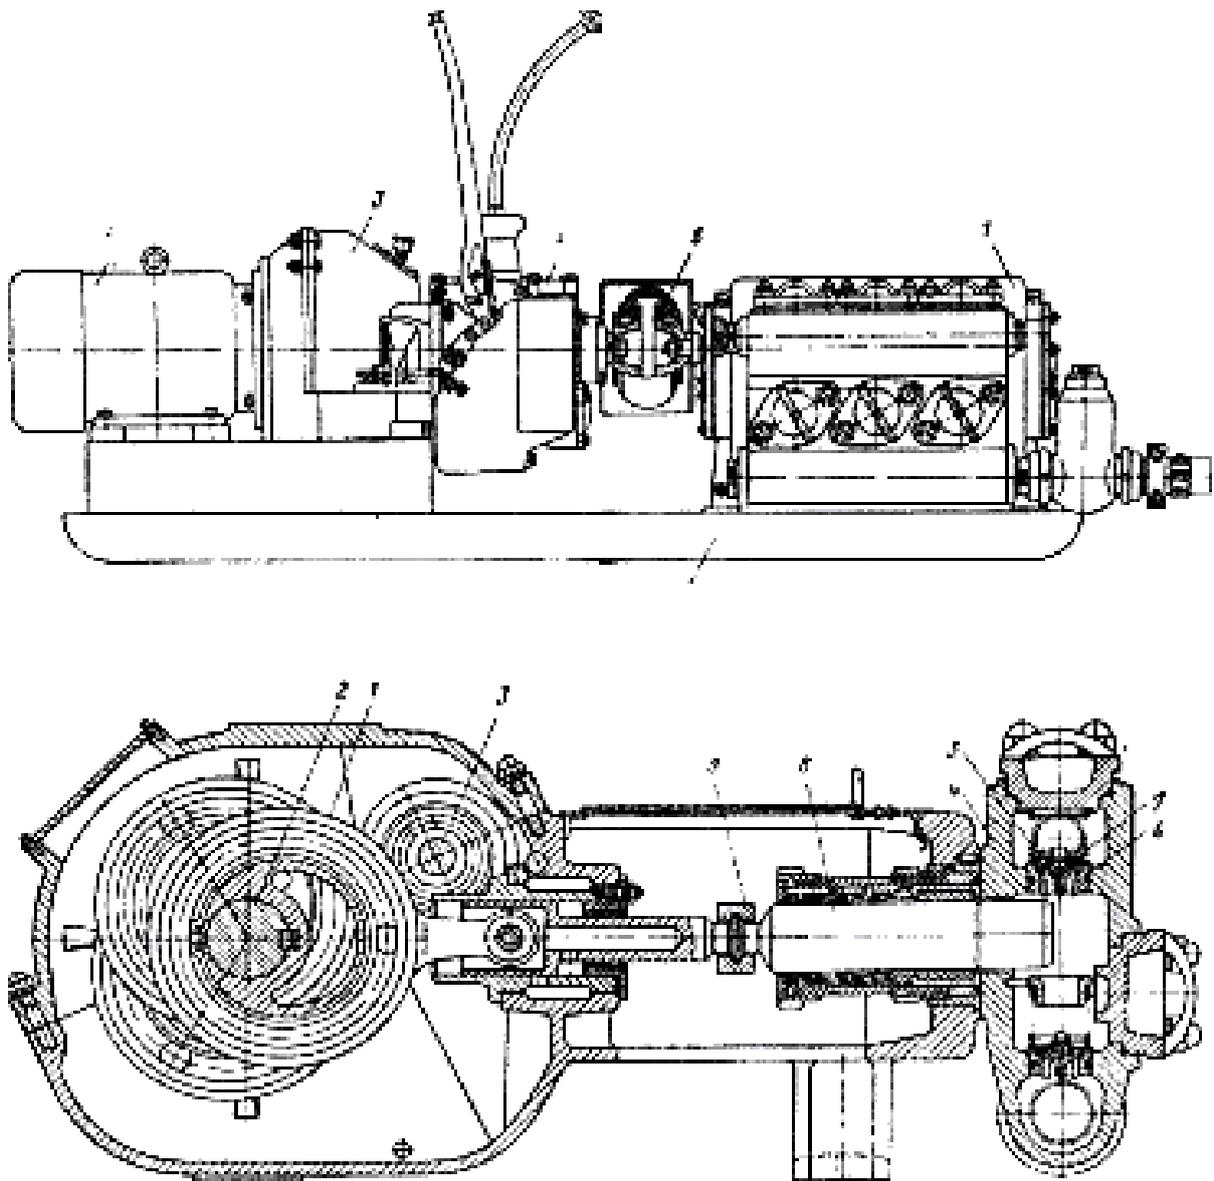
Установка плунжерного насоса. Продольный разрез бурового насоса: 1 – кривошипно-шатунный механизм; 2 – эксцентриковый вал; 3 – входной вал-шестерня; 4 – гидравлическая часть насоса; 5 – клапаны; 6 – седла; 7 – пружины; 8 – плунжера; 9 – хомуты; 10 – крышки
